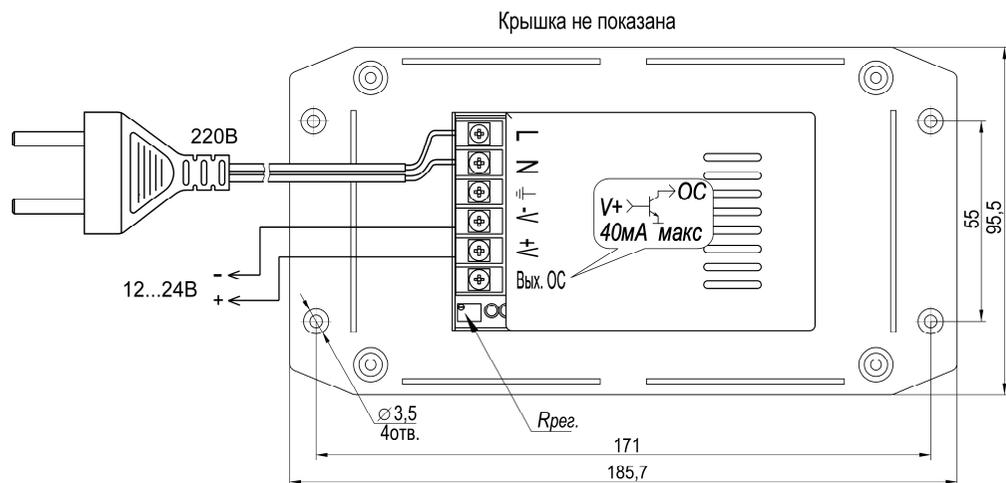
Устройство, габаритные и установочные размеры, подключение изделия
